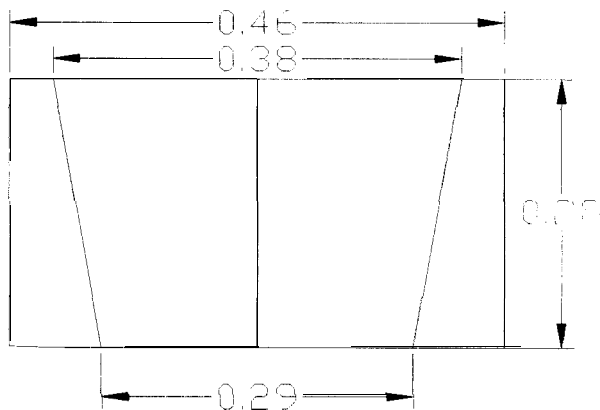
Dimensiones del Recipiente con Chaqueta
